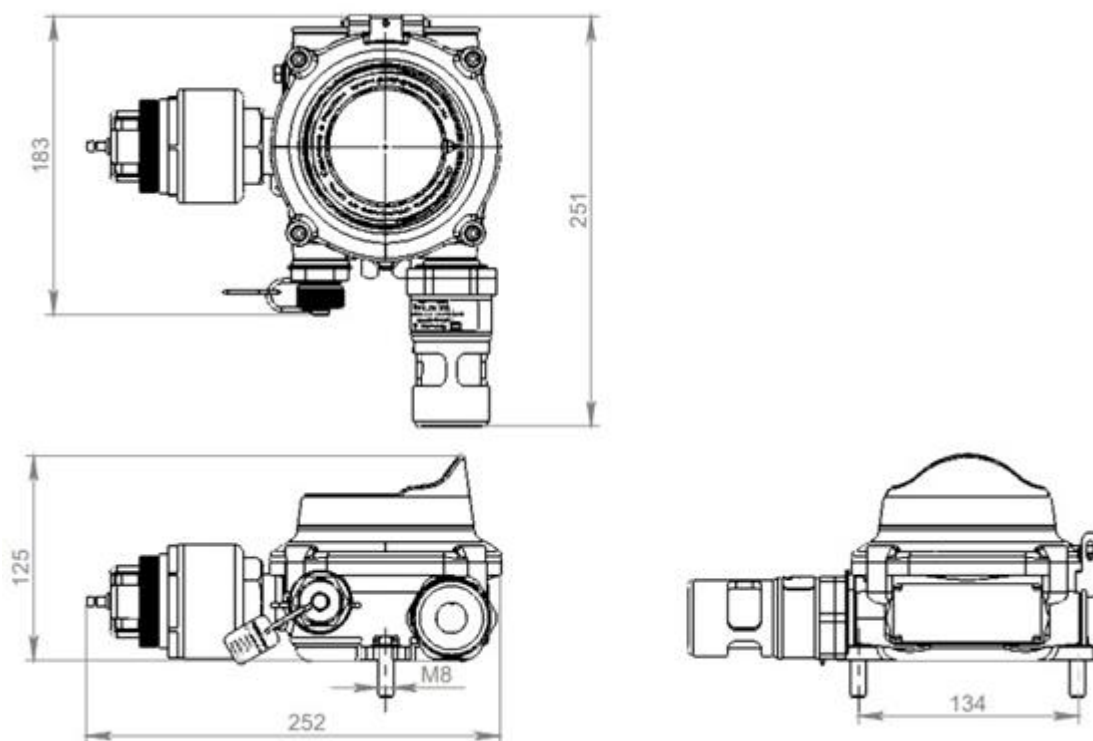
Габаритный чертёж изделия с 5-ю вводными отверстиями с дополнительными принадлежностями
